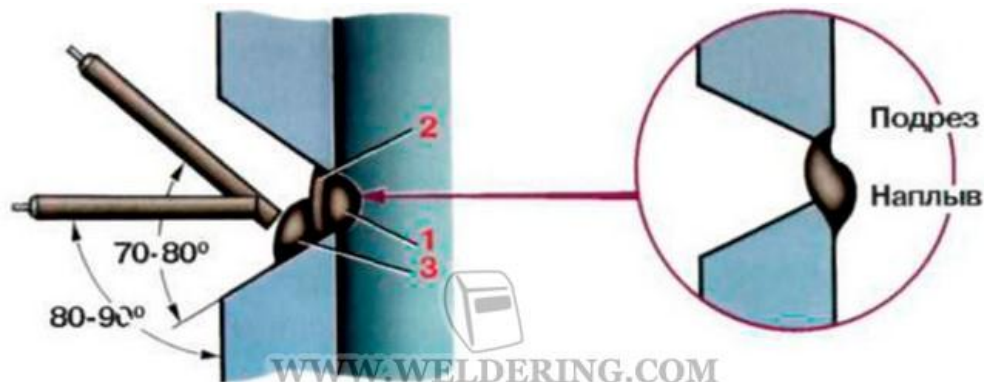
Техника сварки неповоротных горизонтальных стыков труб
